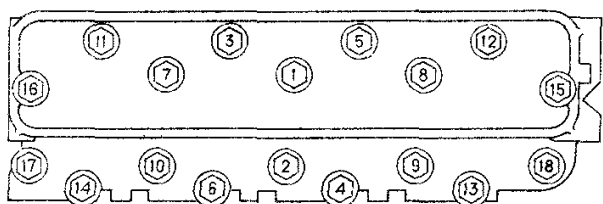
Порядок затяжки гаек крепления головки цилиндров
